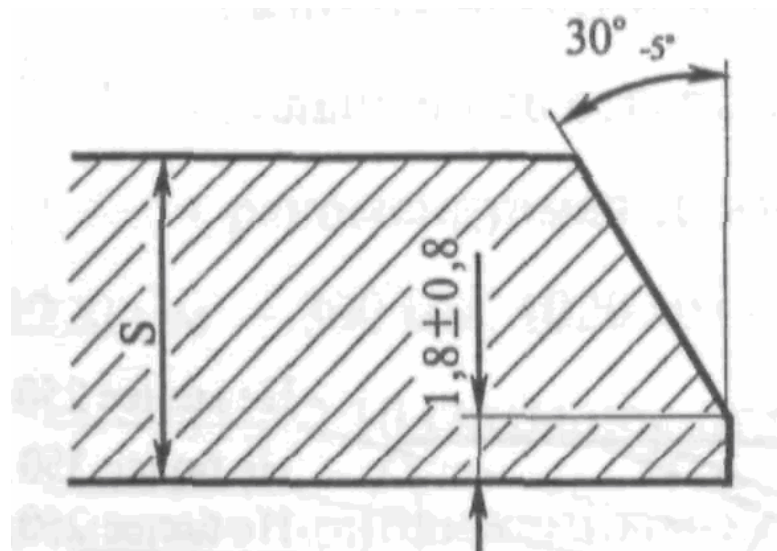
Геометрические параметры разделки кромок торцов труб для ручной дуговой сварки покрытыми электродами после разделительной резки и механической обработки
